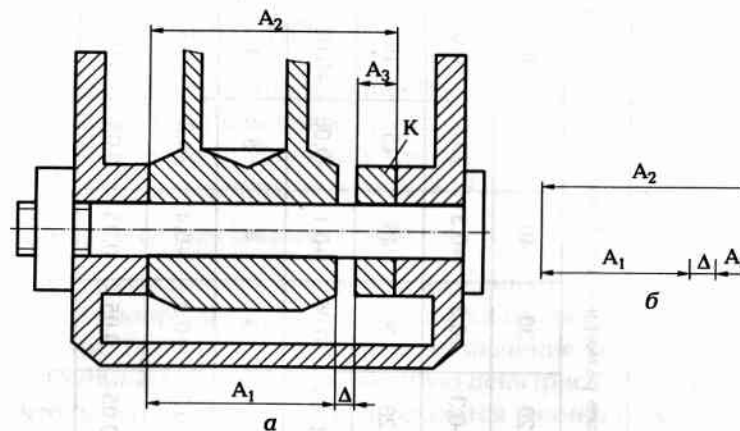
Сборочная единица с осевым зазором и компенсатором: а — сборочный чертеж; б — схема сборки
